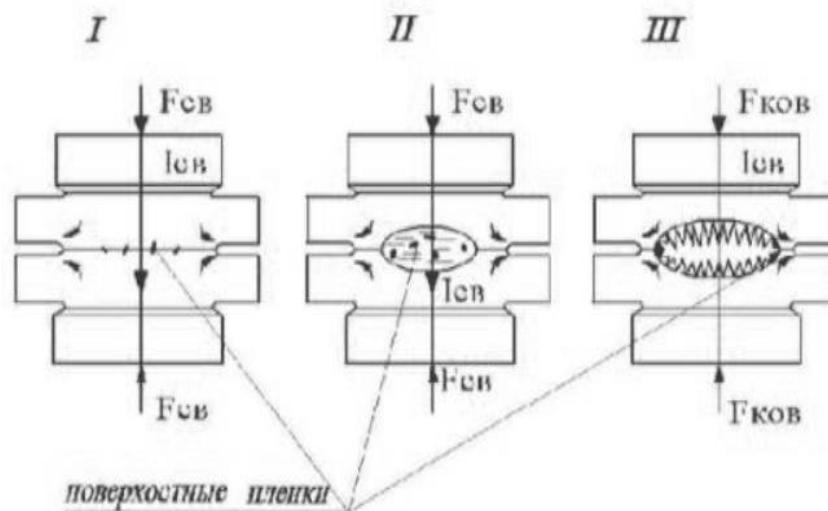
Етапи утворення з'єднання при шовному зварюванні
